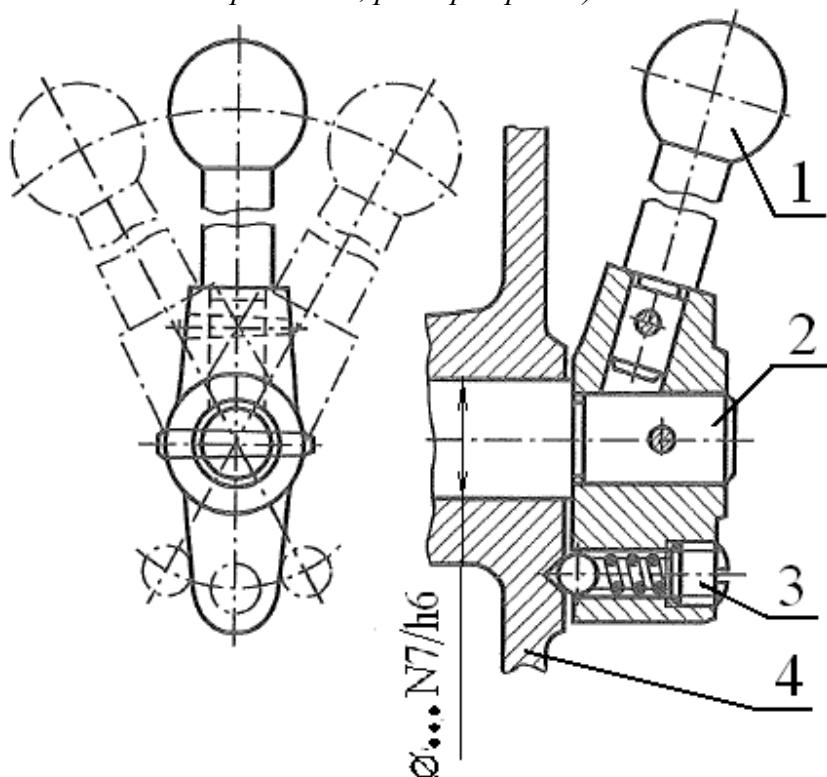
Фиксирующее устройство механизма шариком. Посадка вала 2 в корпус 4 (1- рычаг управления, 3- рычаг с пружиной, входит в гнездо корпуса)
